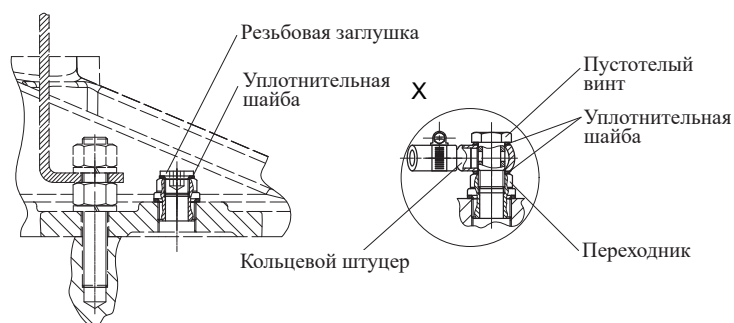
Крепление соединительного шланга к корпусу редуктора
